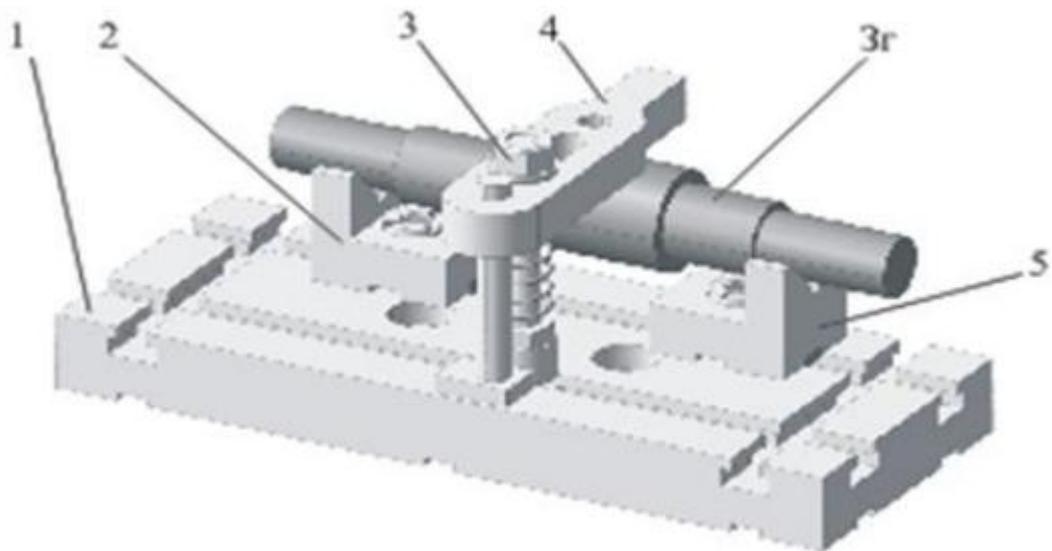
Приспособление для фрезерования пазов на валу:
